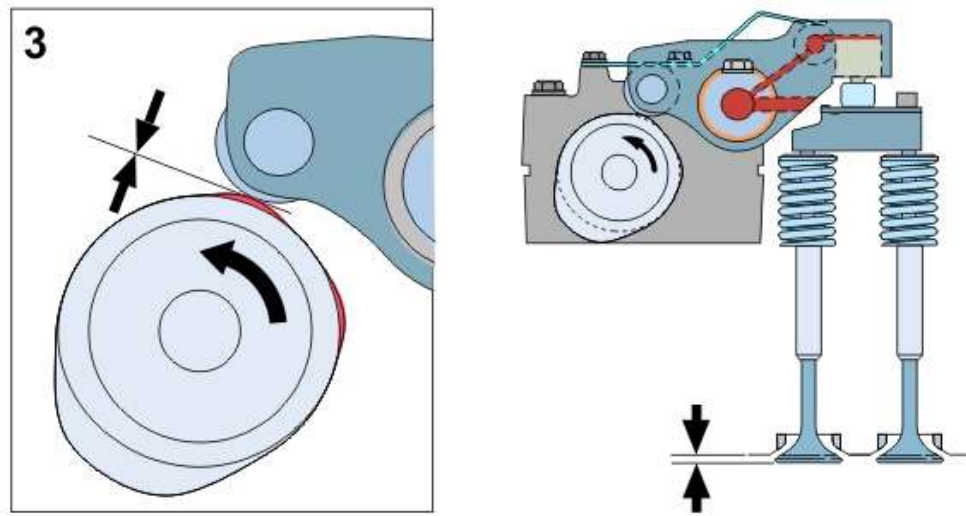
Зміна фаз газорозподілу моторного гальма Volvo Engine Brake +
